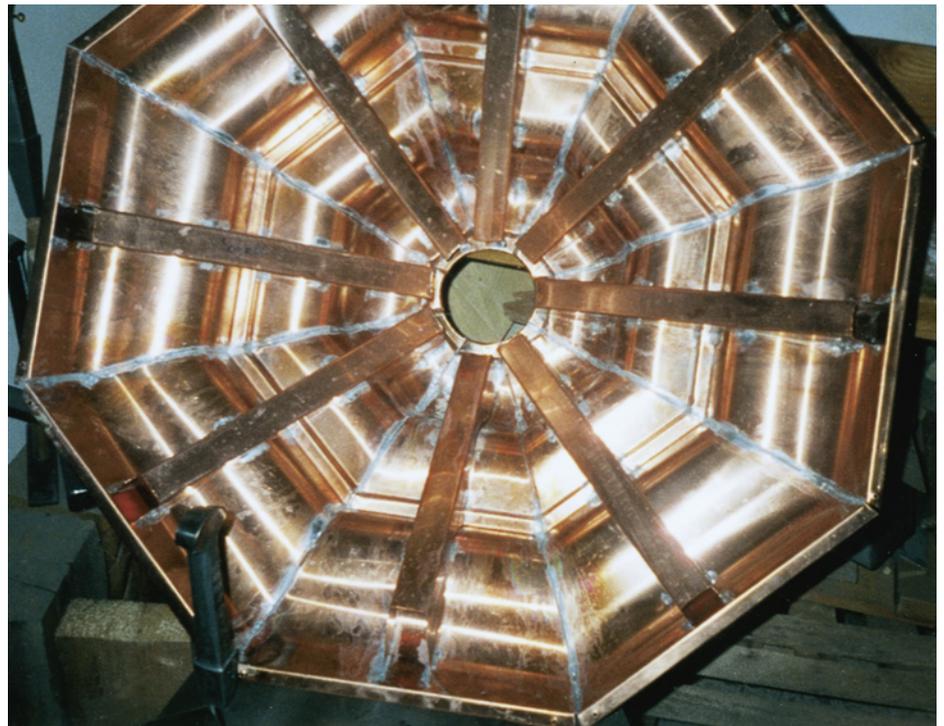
Innenansicht des fertigen Sockels mit seinen gekanteten U-Profilen zur besseren Aussteifung.
